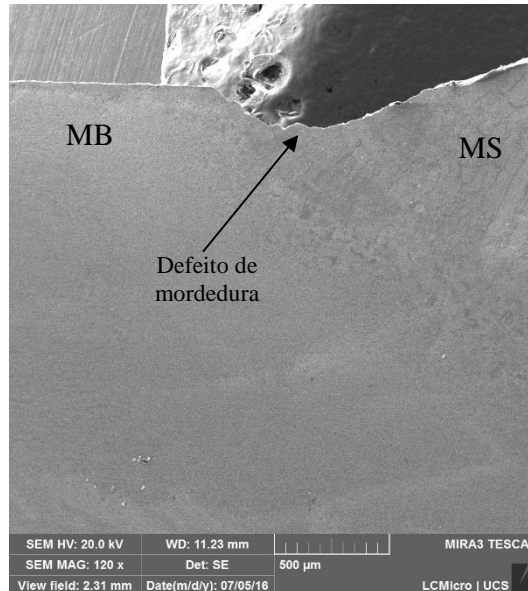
Defeito de mordedura entre metal base e metal de solda
